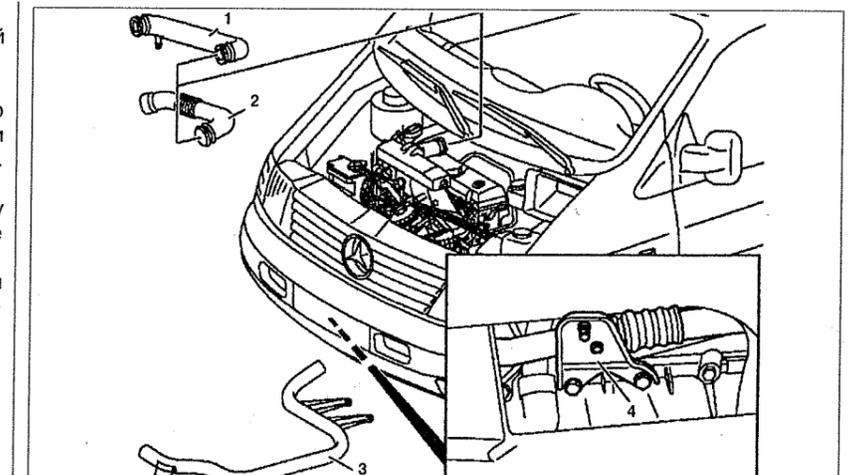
Поддон: 1. Верхняя трубка подачи сжатого воздуха, 2. Воздушная впускная труба, 3. Нижняя трубка подачи сжатого воздуха, 4. Кронштейн крепления трубок системы кондиционирования.
